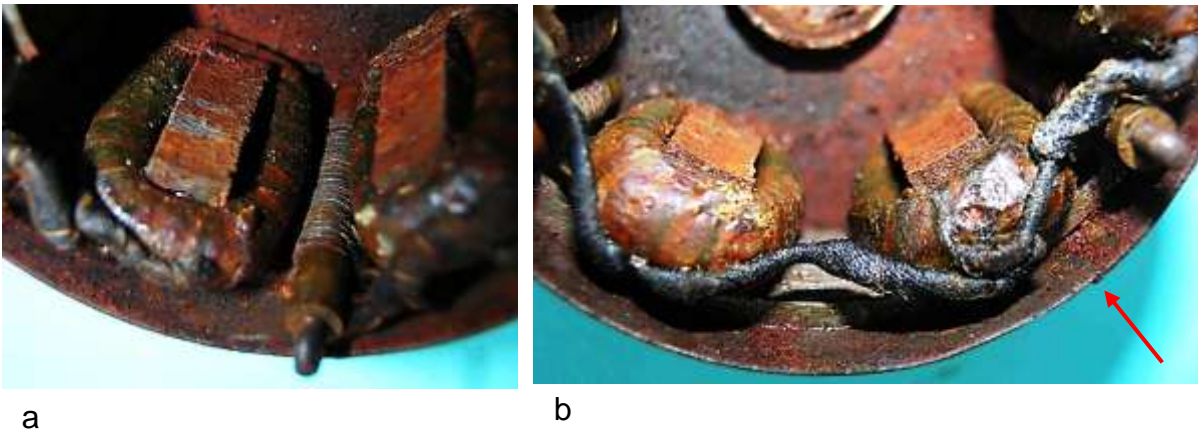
Gehäusemantel und Anker: a) Gewindebolzen mit Abstandshülsen, b) Pole und Joch des Ankerpolrings
